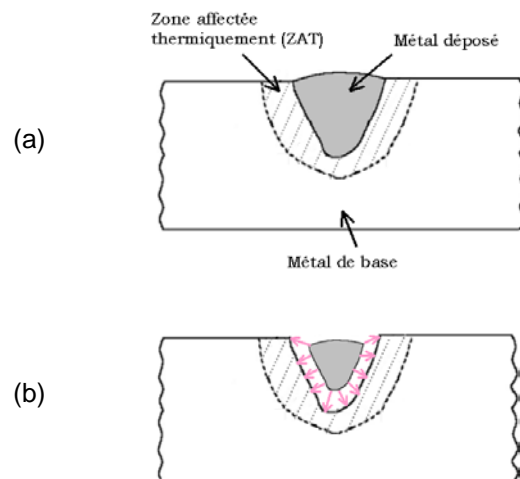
Un cordon de soudure déposé (a) avant et (b) après le refroidissement complet
